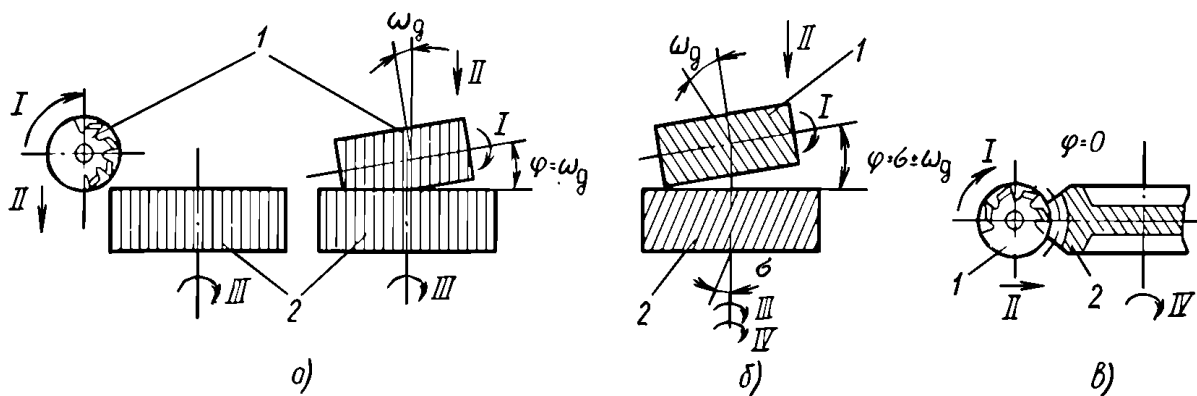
Схема роботи черв'ячної модульної фрези: а – при нарізанні циліндричних прямозубих коліс; б - при нарізанні циліндричних коліс з гвинтовим зубом; в - при нарізанні черв'ячних коліс. 1 – фреза, 2 – заготовка.
